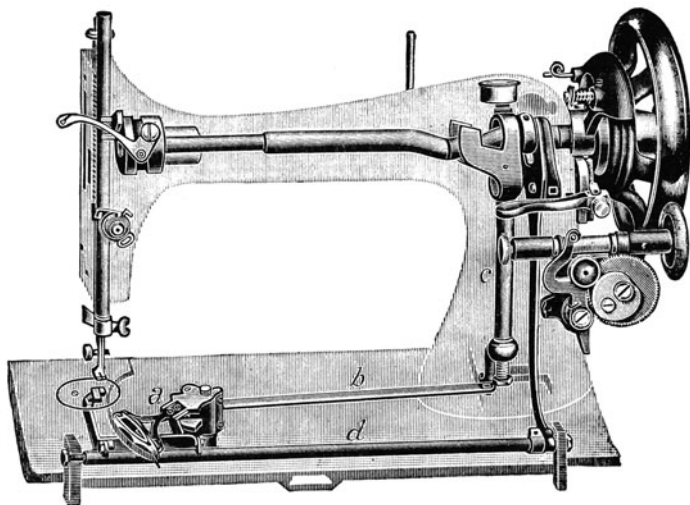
Das Getriebe einer Bogenlangschiffchen-Maschine.
